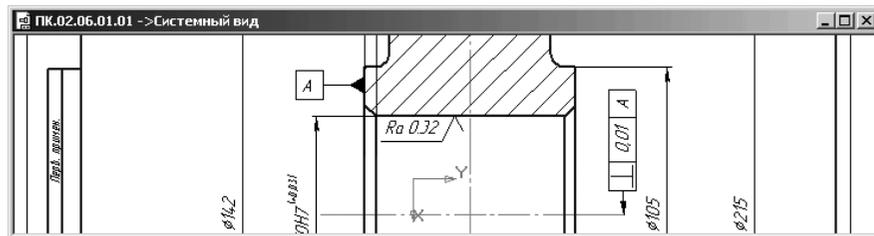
Фрагмент чертежа с обозначением допуска формы
